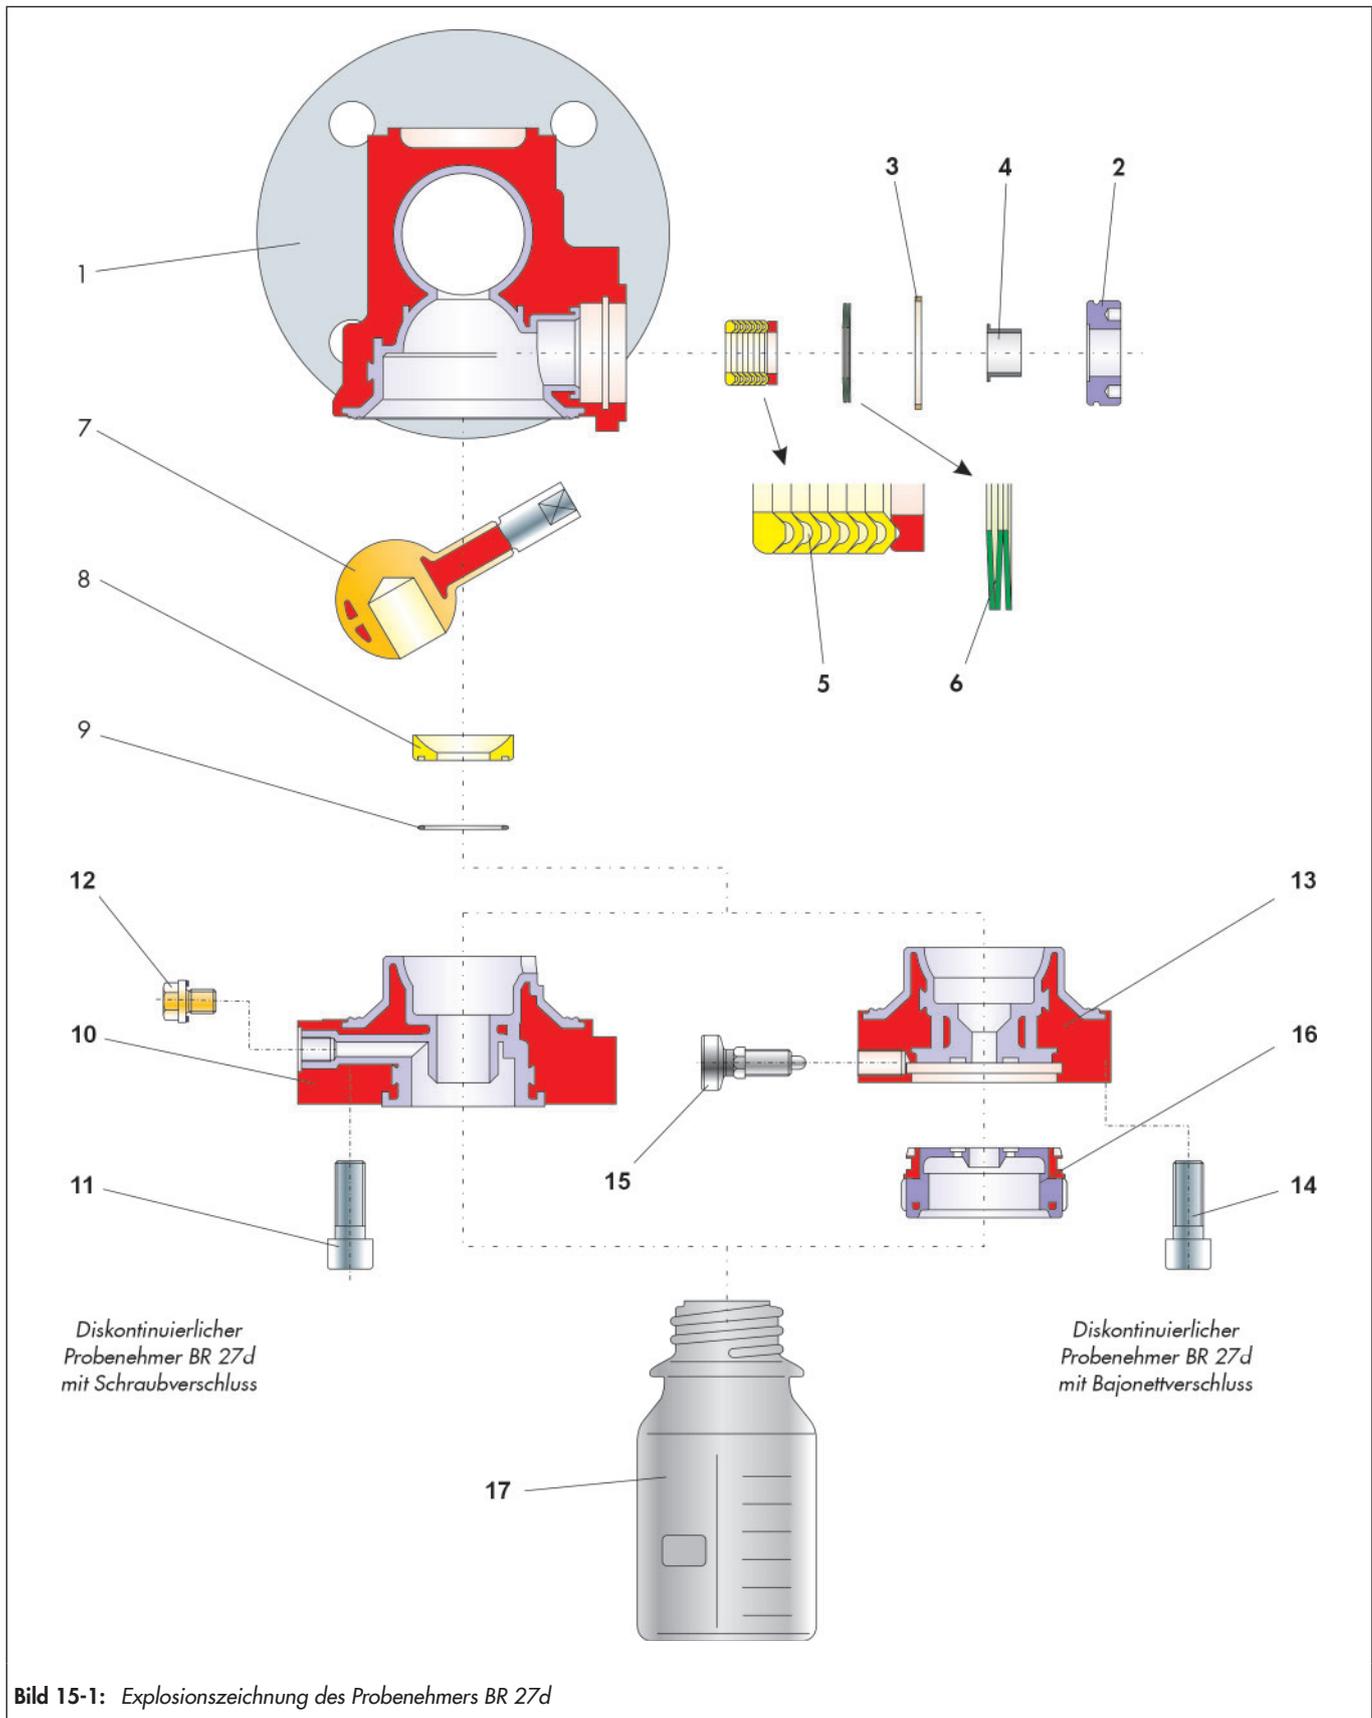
Explosionszeichnung des Probenehmers BR 27d
